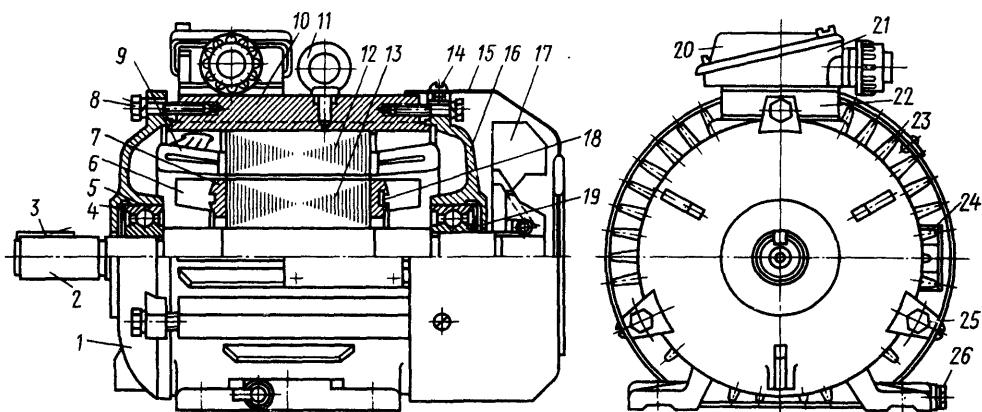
Асинхронный закрытый двигатель с короткозамкнутым ротором
